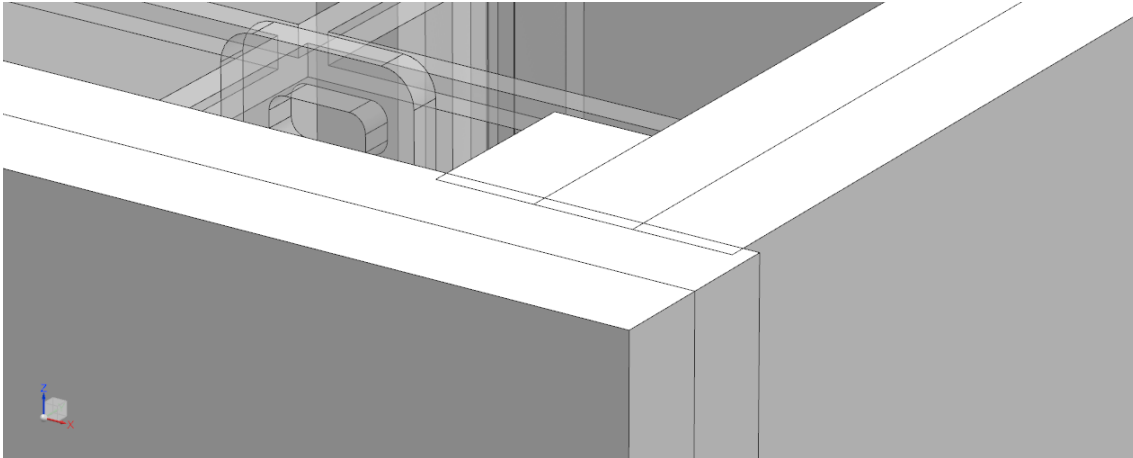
Sobredimensionado para materiales por corte láser / Fuente: Propia
